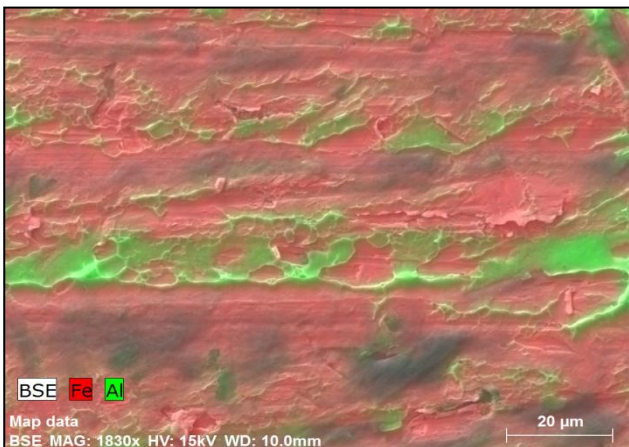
Superfície de fratura do aço. Soldas com preaquecimento.
